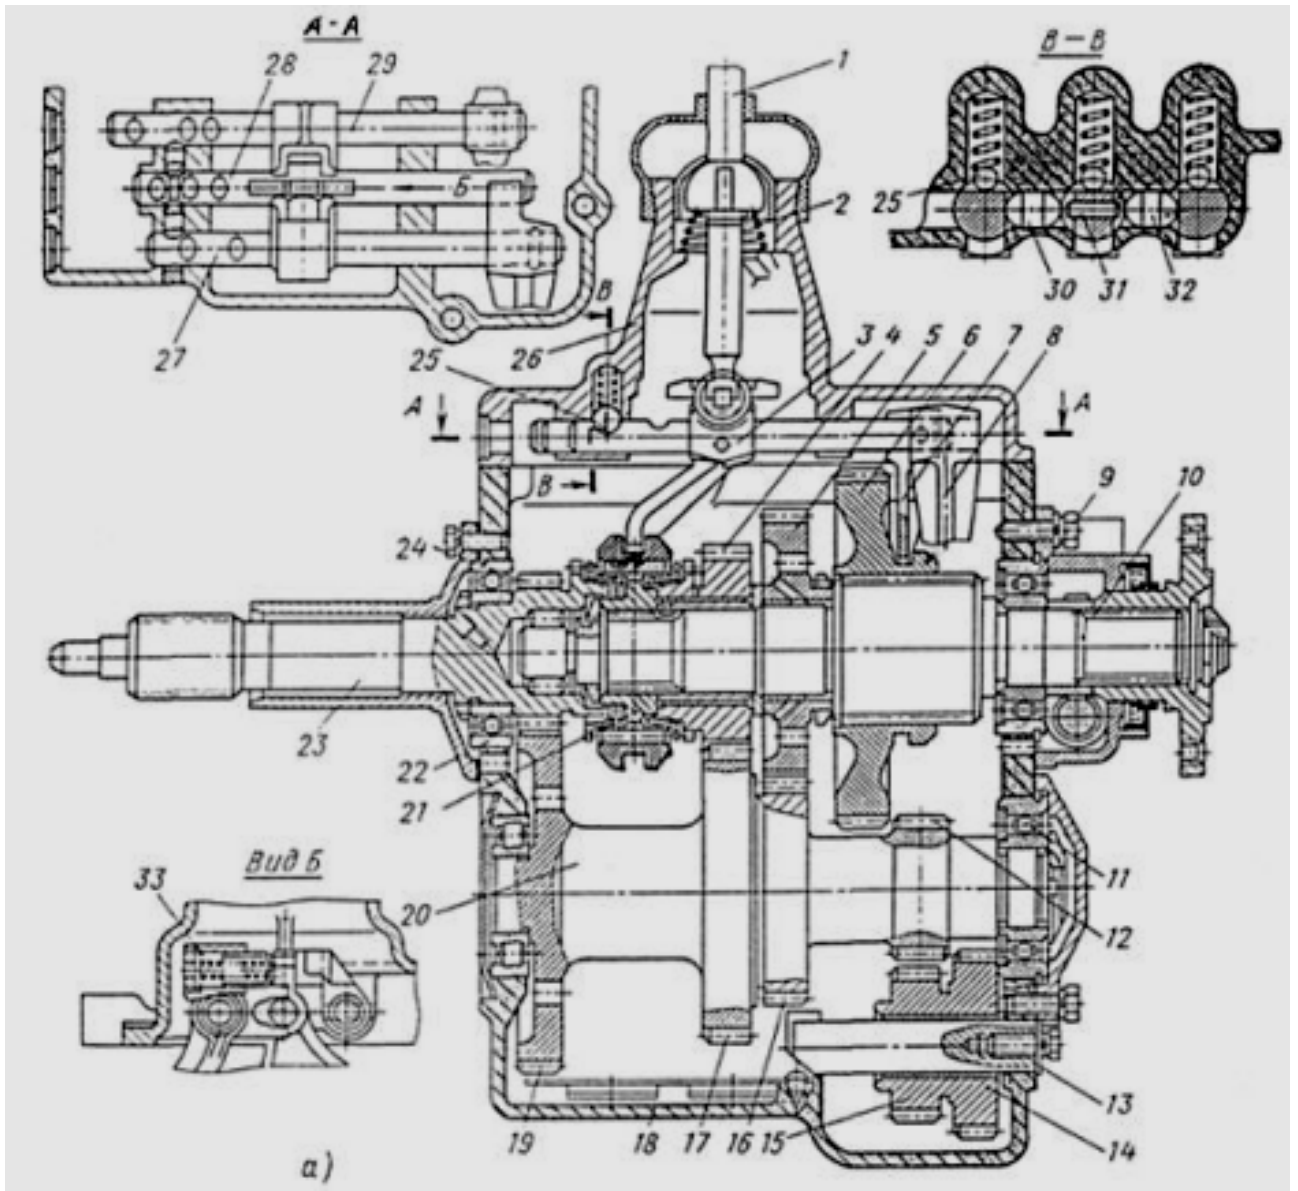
Механизм переключения коробки передач: 1 - рычаг; 2 - пружина; 3, 7, 8 - вилка; 4, 17 - шестерня и колесо третьей передачи; 5, 16 - колесо и шестерня второй передачи; 6 - колесо-каретка первой передачи и заднего хода; 9, 11, 22 - шариковые подшипники; 10 - ведомый вал; 12 - зубчатое колесо; 13 - ось; 14, 15 - зубчатое колесо заднего хода; 18 - корпус; 19 - зубчатое колесо; 20 - промежуточный вал; 21 - ступица синхронизатора; 23 - ведущий вал; 24 - шестерня ведущего вала; 25 - шариковый фиксатор; 26 - крышка с механизмом переключения передач; 27, 28, 29 - ползун; 30, 32 - сухарь; 31 - штифт; 33 - пружинный предохранитель
